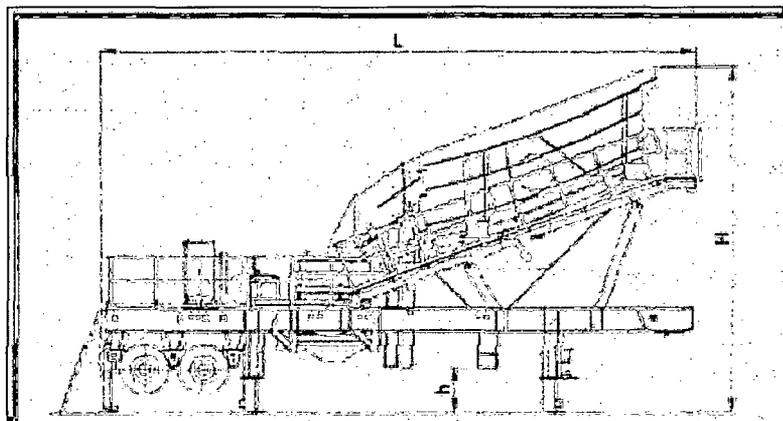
Vista del montaje de operación de la planta trituradora portátil según fabricante
